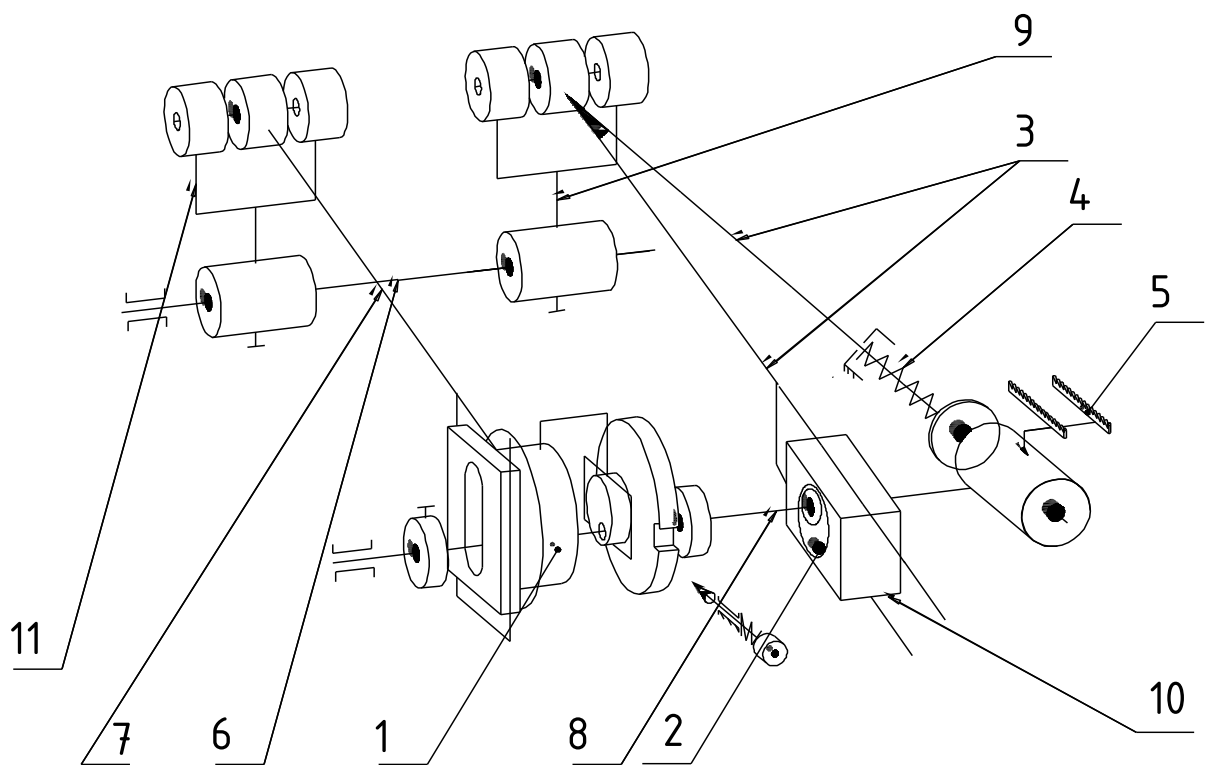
Кінематична схема механізму зубчатої рейки машини 1776 (II)
